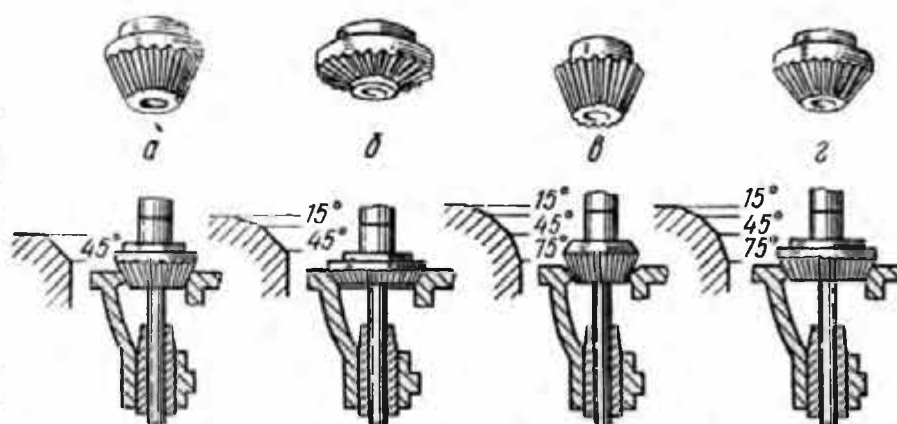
Обробка клапанного гнізда фрезами. Фрезерування під кутом:
